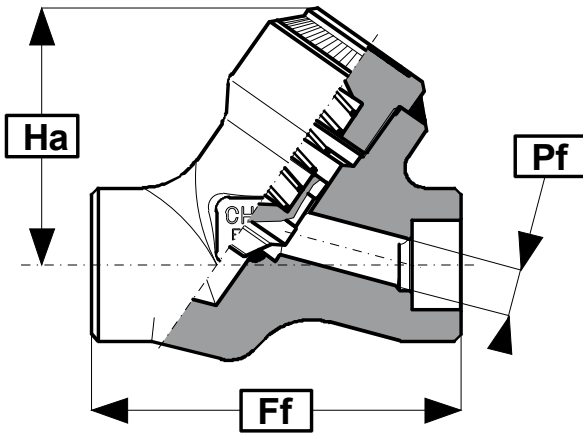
WC - RETENCIÓN A PISTÓN 'Y' A105/F6 TRIM Nº 1 - 2500LBS SW WELDED COVER
